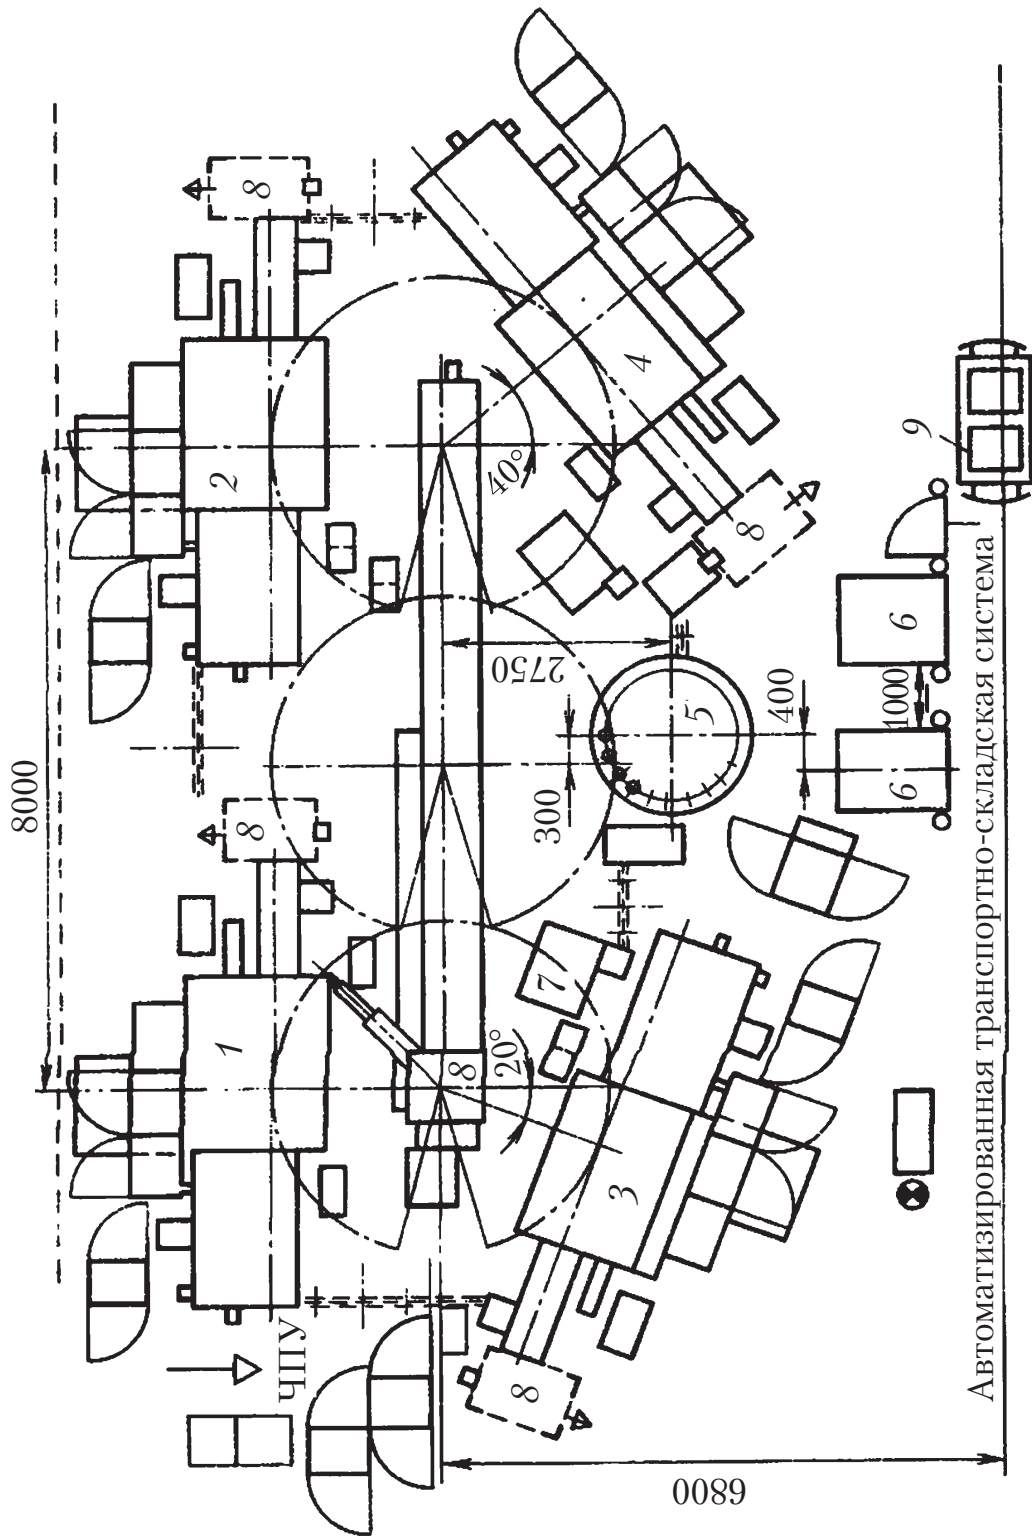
Планировка РТК для патронного изготовления деталей типа тел вращения
